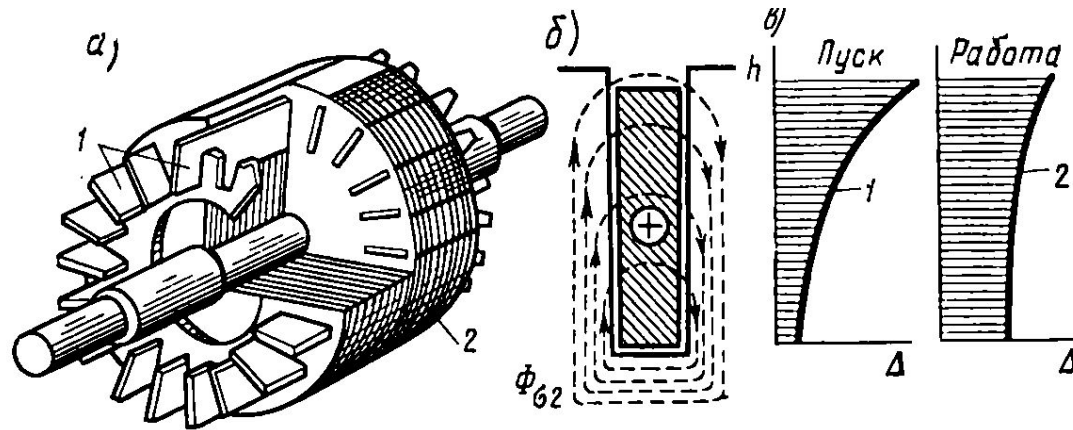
Общий вид (а), разрез паза (б) ротора глубокопазного двигателя и разновидности пазов глубокопазных двигателей (в):
